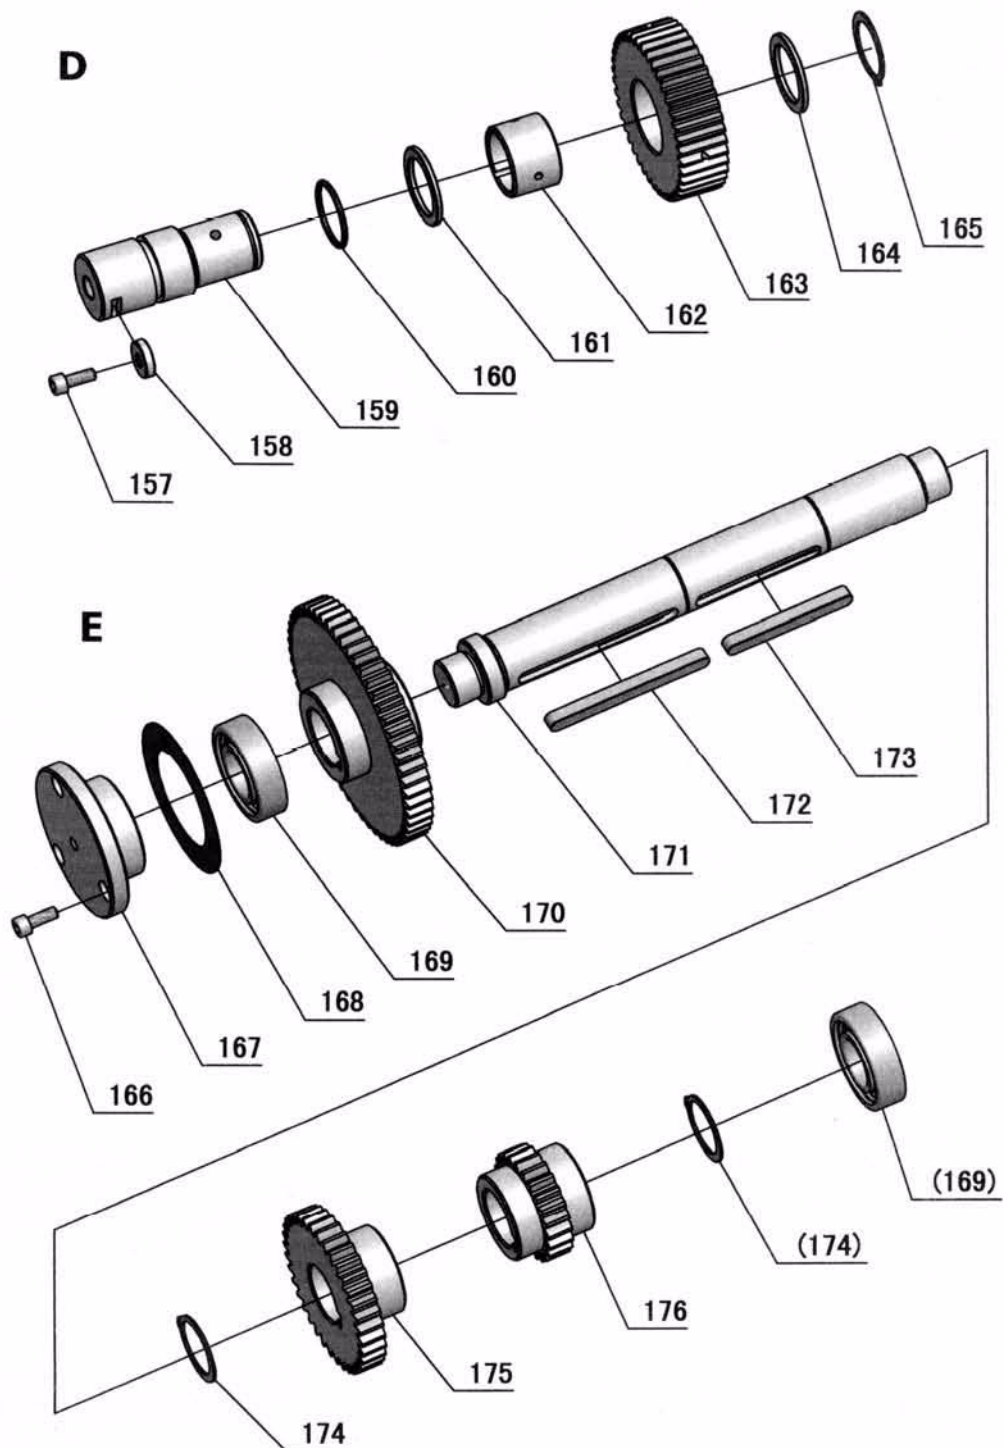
Spindelstock 6 von 8 - Headstock 6 of 8
